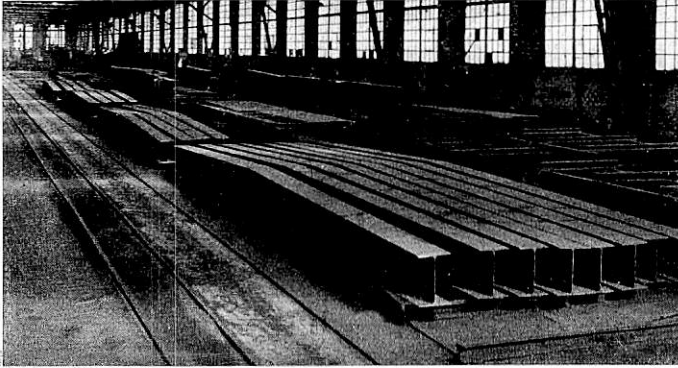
Dachförmige, geschweißte Träger.
